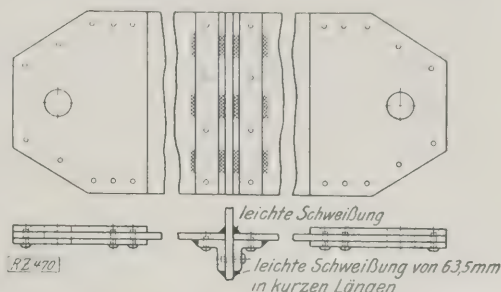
Zwei Bleche mit dem senkrechten Blech durch Nieten und Schweißung verbunden.
